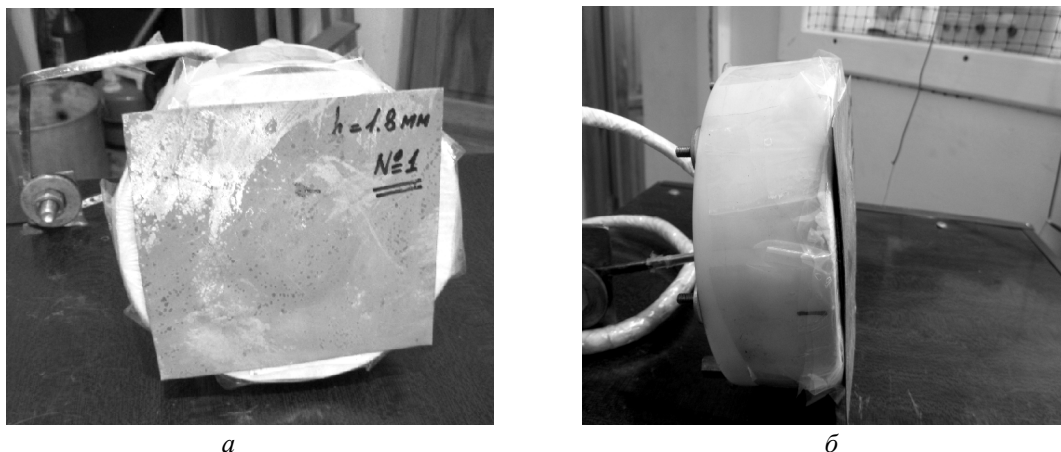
Ілюстрація практичного здійснення експерименту (листова заготовка з оцинкованої сталі на робочій поверхні ІСЕР): а – зразок з вм'ятиною до силового впливу; б – вирівняна листова заготовка після магнітно-імпульсного притягання
